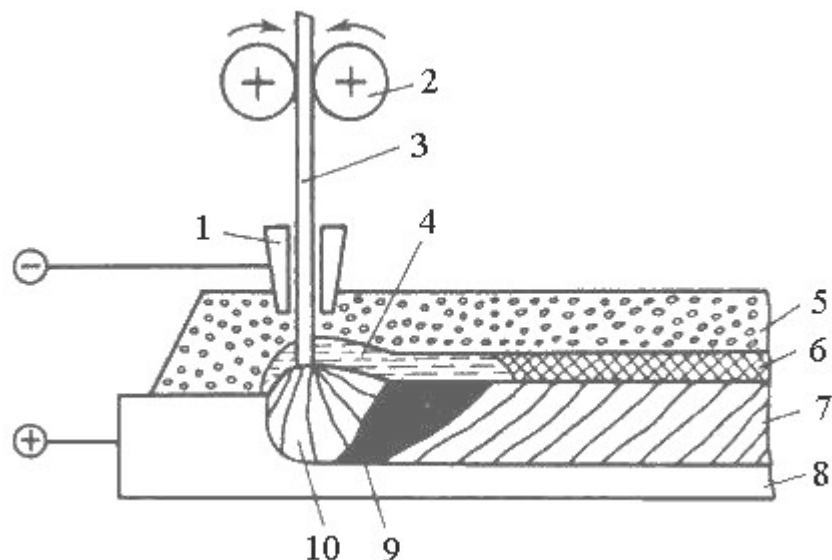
Схема автоматической дуговой сварки под флюсом: 1 – токопровод; 2 – механизм подачи проволоки; 3 – проволока; 4 – жидкий шлак; 5 – флюс; 6 –шлаковая корка; 7 – сварной шов; 8 – основной металл; 9 – ванна жидкого металла; 10 – дуга
